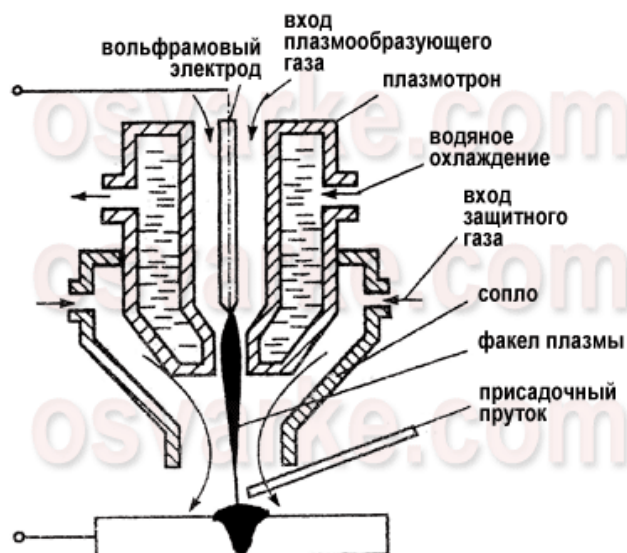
Схема выполнения плазменной сварки
